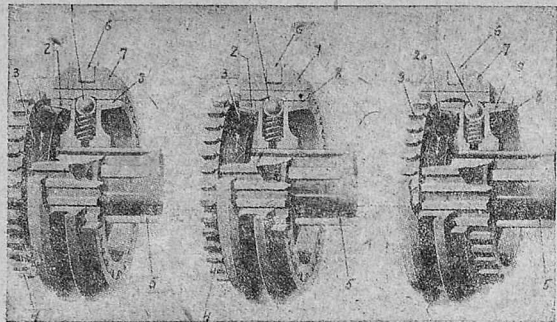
Включение прямой передачи с синхронизатором. 1—стопор-синхронизатора, 2—конус подвижной шестерни, 3—конус шестерни постоянного зацепления, 4—шестерня постоянного зацепления, 5—вторичный вал, 6—подвижная шестерня, 7—подвижная муфта, 8—вилка переключения
